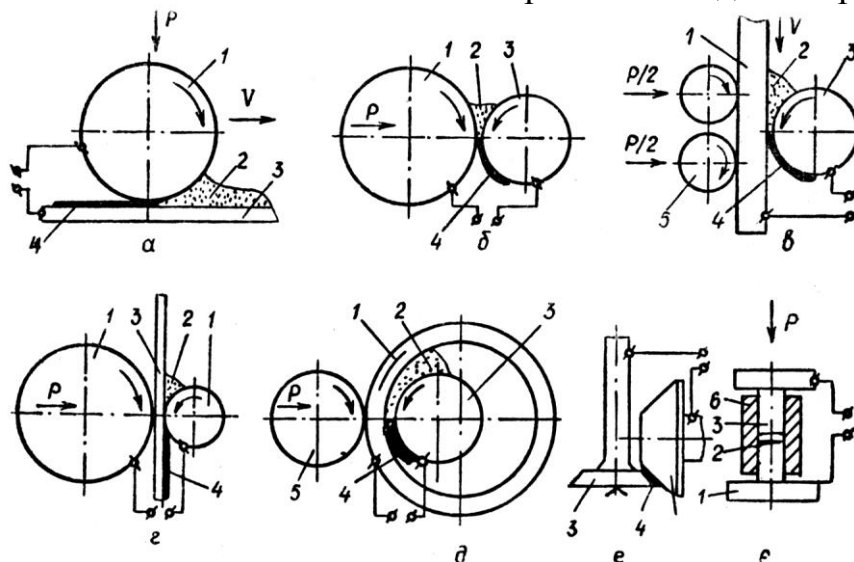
Схеми електроконтактного напикання металічних порошків: а, в, в, г, д, е, ж — варіанти; 1 — контактний ролик електрод; 2 — металічний порошок; 3 — деталь; 4 — напечений шар порошку; 5 — натискний ролик; 6 — форма
